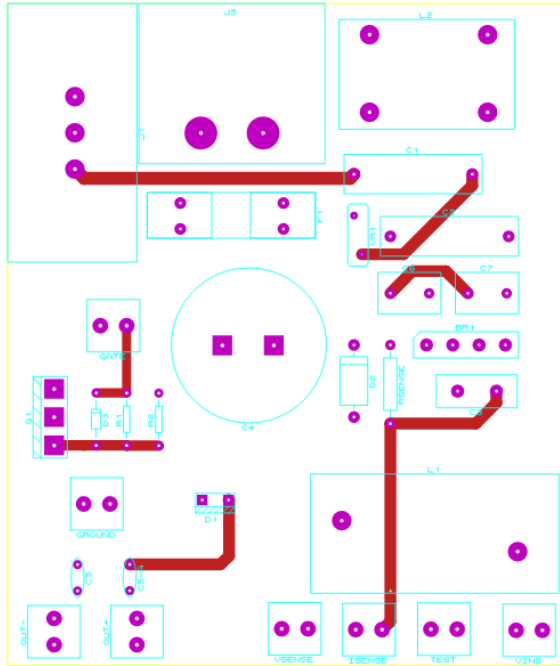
Cara Frontal del PCB del circuito de fuerza, prototipo final
